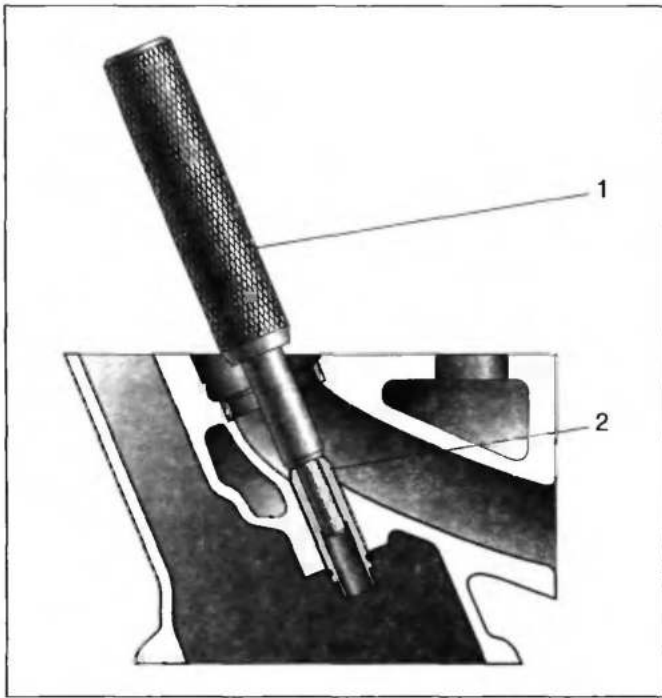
Оправка для выпрессовки направляющей втулки клапана ударным способом:
